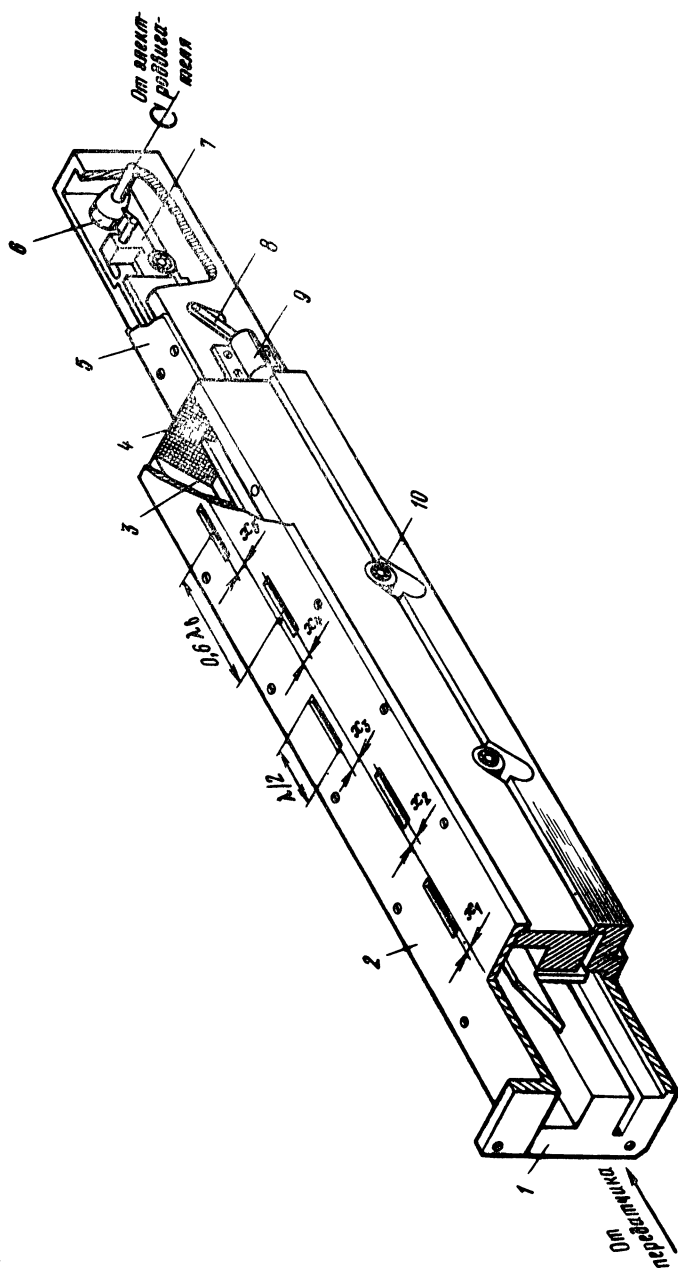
Конструкция ВЩР с электромеханическим сканированием:
